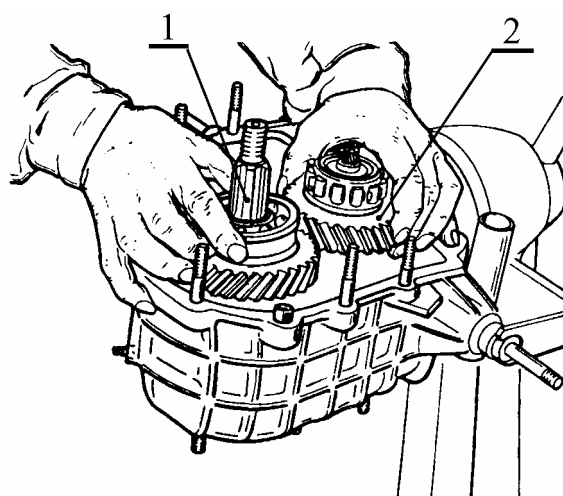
Установка в картер раздаточной коробки ведущего и промежуточного валов:
